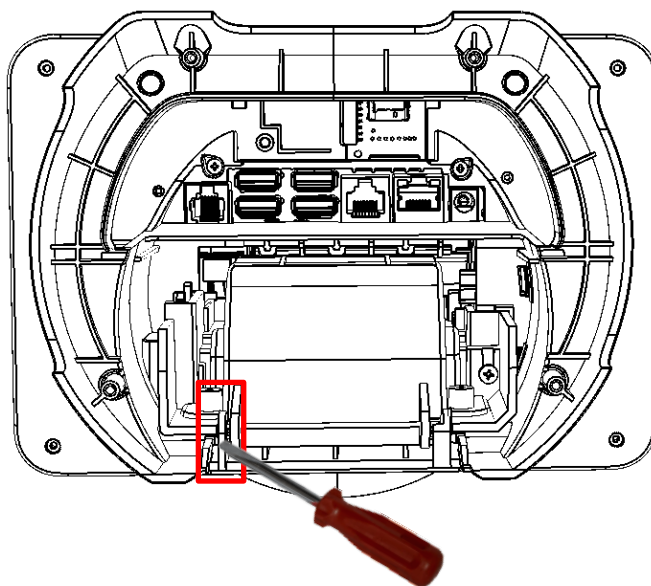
Место соединения фиксатора крышки и цилиндрического держателя
